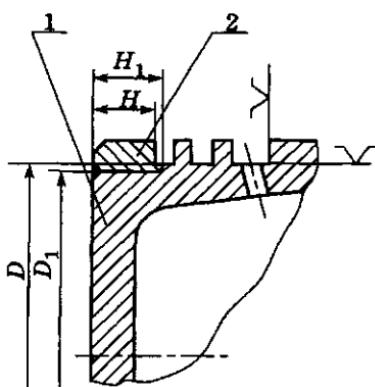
Схема установки ДРД при восстановлении канавки поршня:
